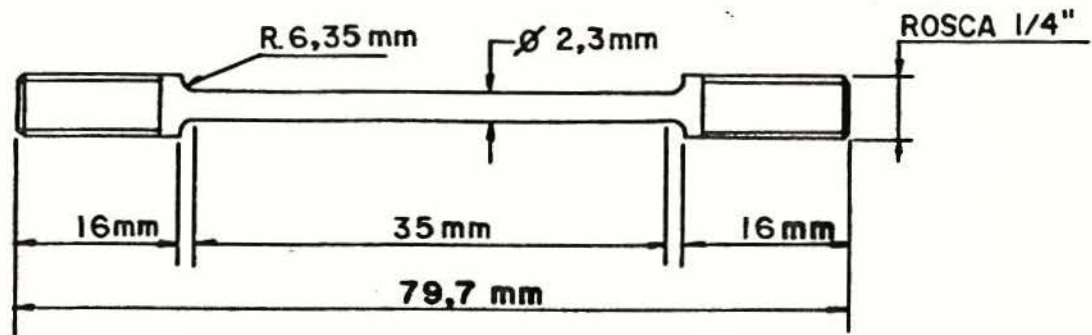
Desenho esquemático das dimensões do corpo de prova.
